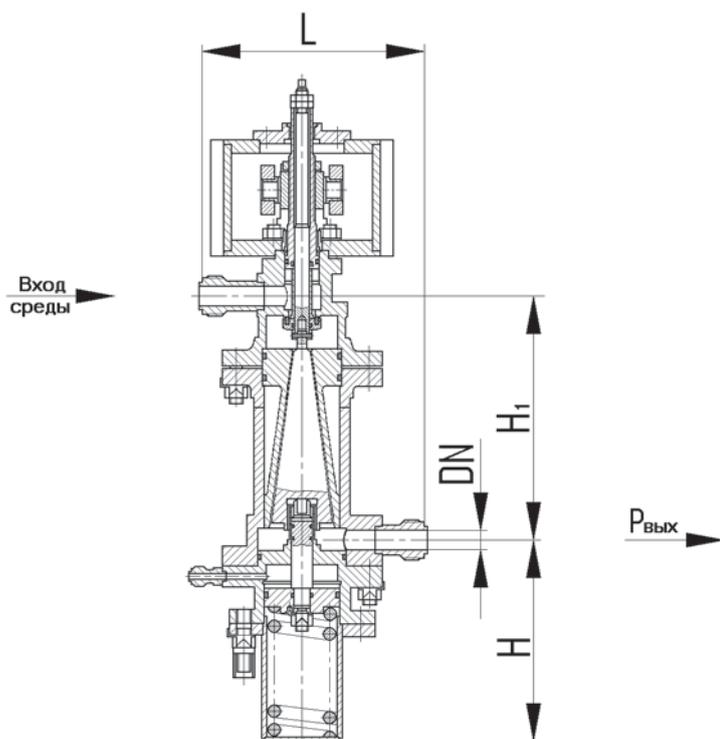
Клапан регулирующий проходной штуцерный
